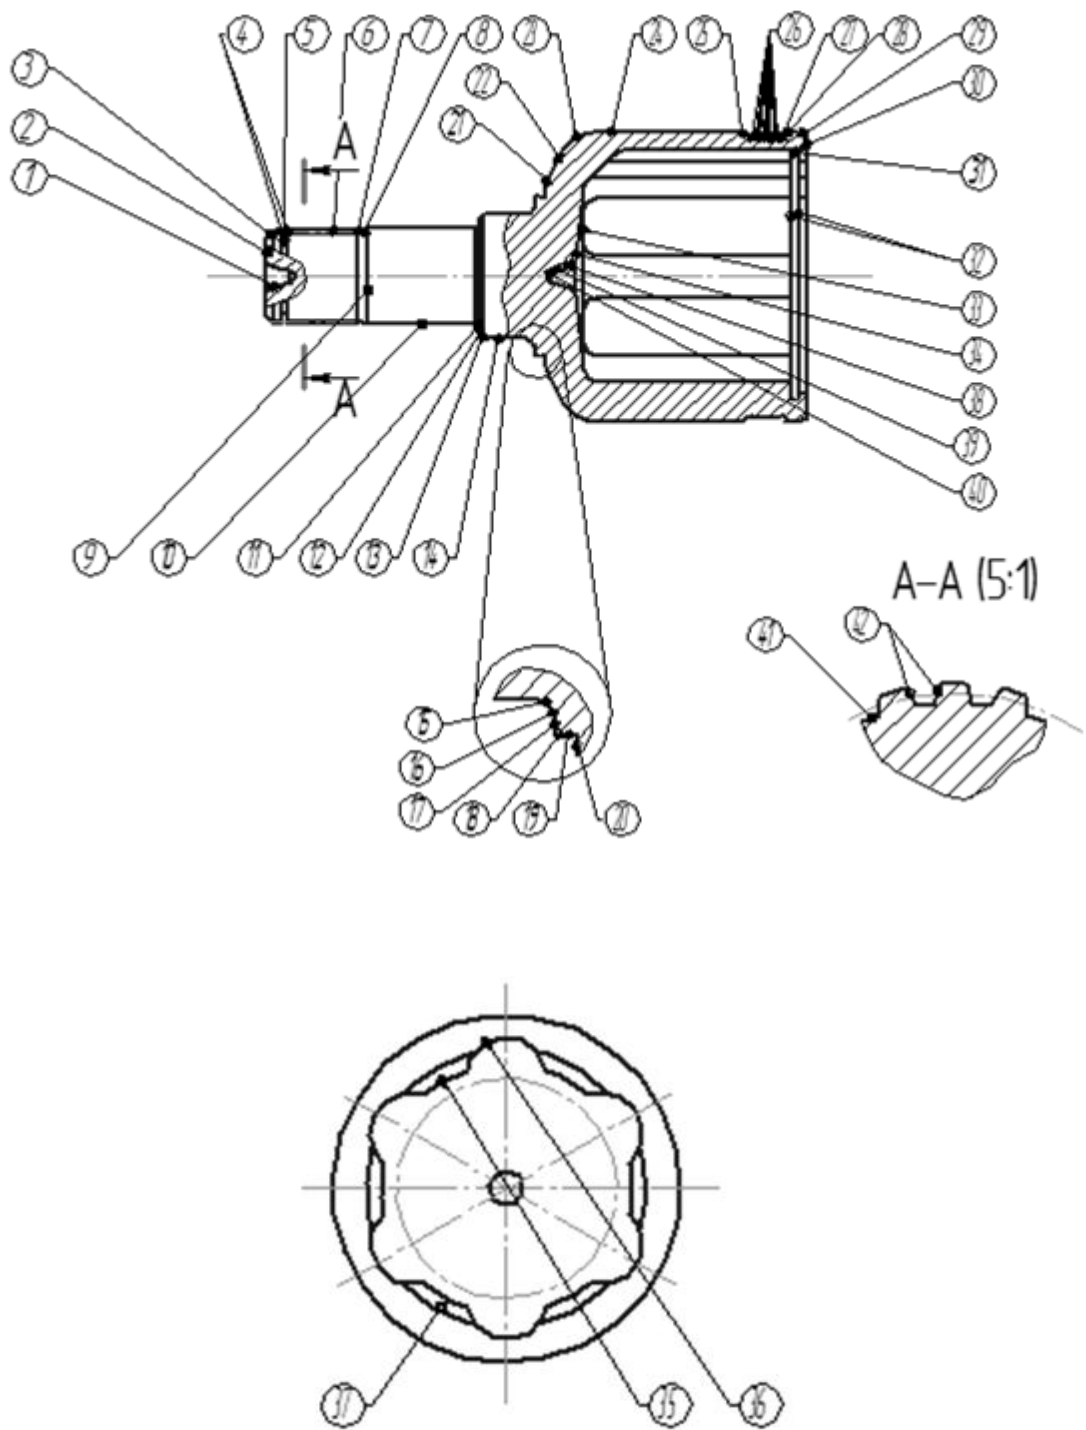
Нумерация поверхностей детали корпус внутреннего шарнира
